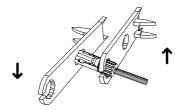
Fixieren des Kabels mit der Kabelverschraubung
